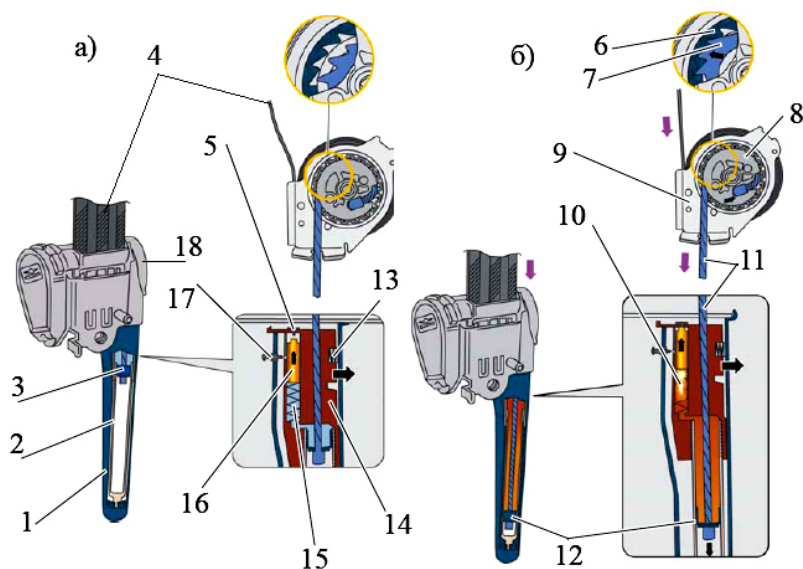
Тросовый натяжитель: 1 – защитная трубка; 2 – трубка; 3,12 – поршень; 4 – ремень безопасности; 5 – отбойная пластина с ударным штифтом; 6 – зубчатое кольцо вала; 7 – зубчатый сегмент; 8 – барабан; 9,18 – механизм смотки ремня безопасности; 10,15 – ударная пружина; 11 – стальной трос; 13 – пружина датчика; 14 – кронштейн датчика; 16 – газогенератор; 17 – болт датчика; а – воспламенение; б – натяжение
